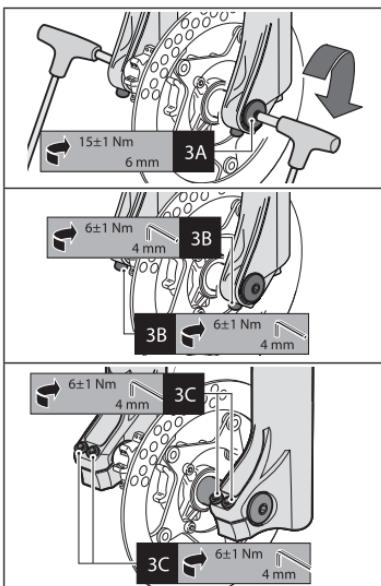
Установка колеса на вилку с осью втулки диаметром Ø20mm
